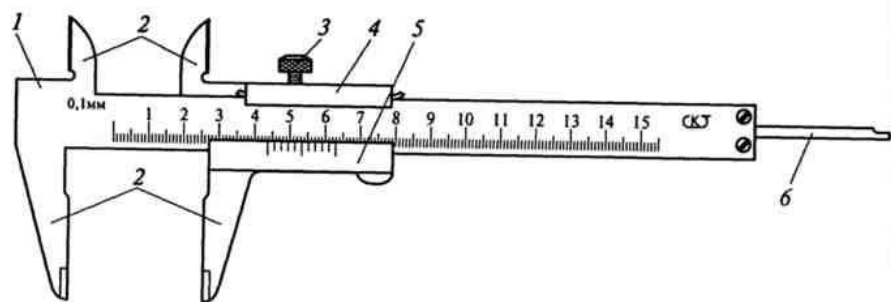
штанга, 2 – губки для внутрішніх вимірювань, 3 затиск рамки, 4- рухлива рама, 5 – ноніус, 6 – лінійка для вимірювання глибин,
